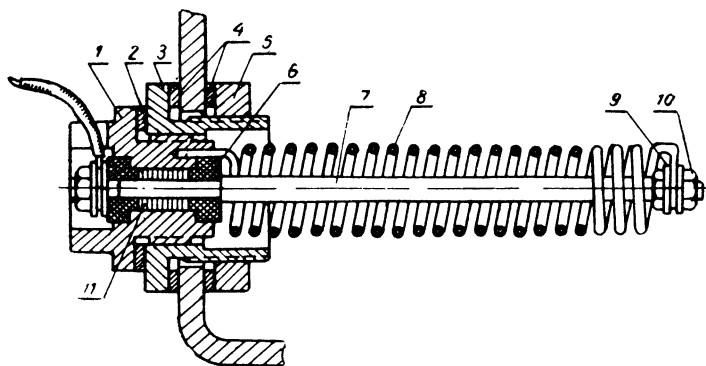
Нагревательный элемент для трактора ДТ-54:
